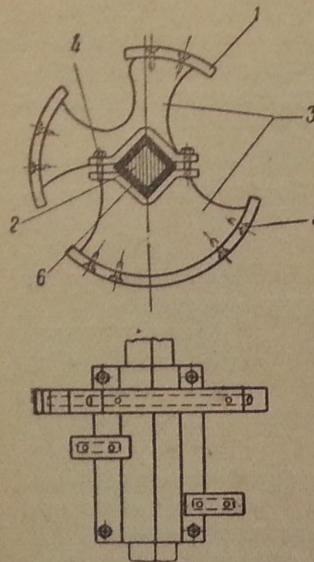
Горизонтальный разрез главного барабана металлической конструкции.
